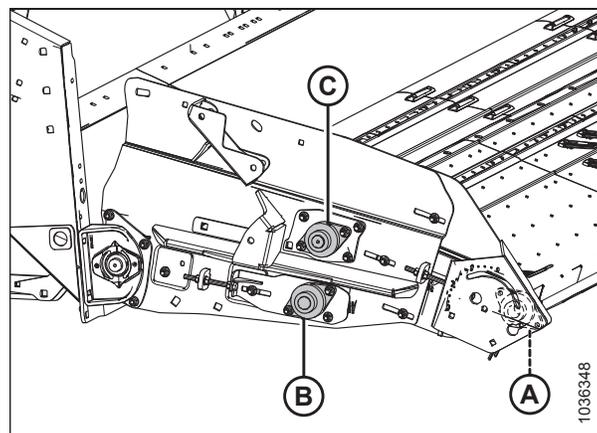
Rodamientos con accesorios de engrase: lado derecho de la plataforma
